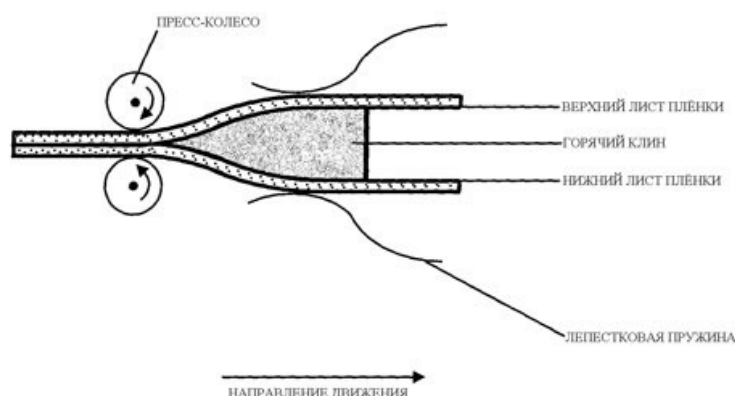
Схема работы аппарата горячей сварки [117]
